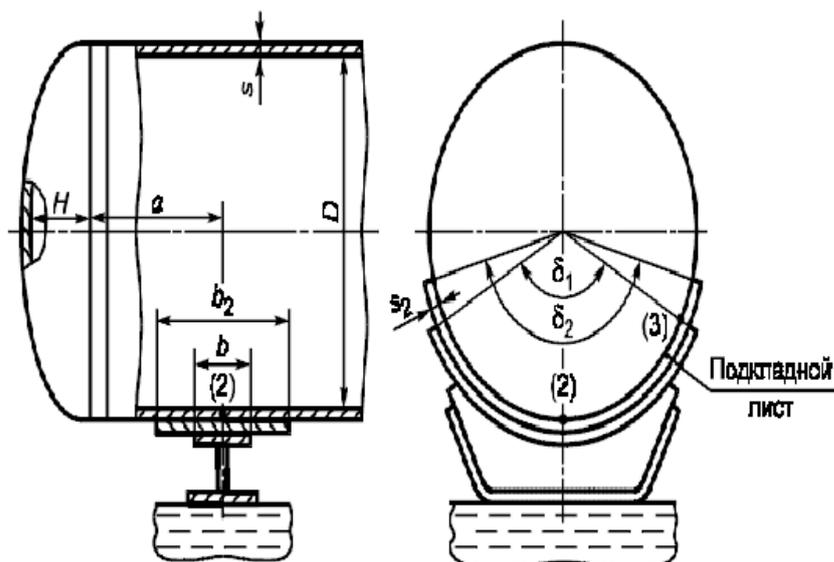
Расчетная схема обечайки не подкрепленной кольцами жесткости.
